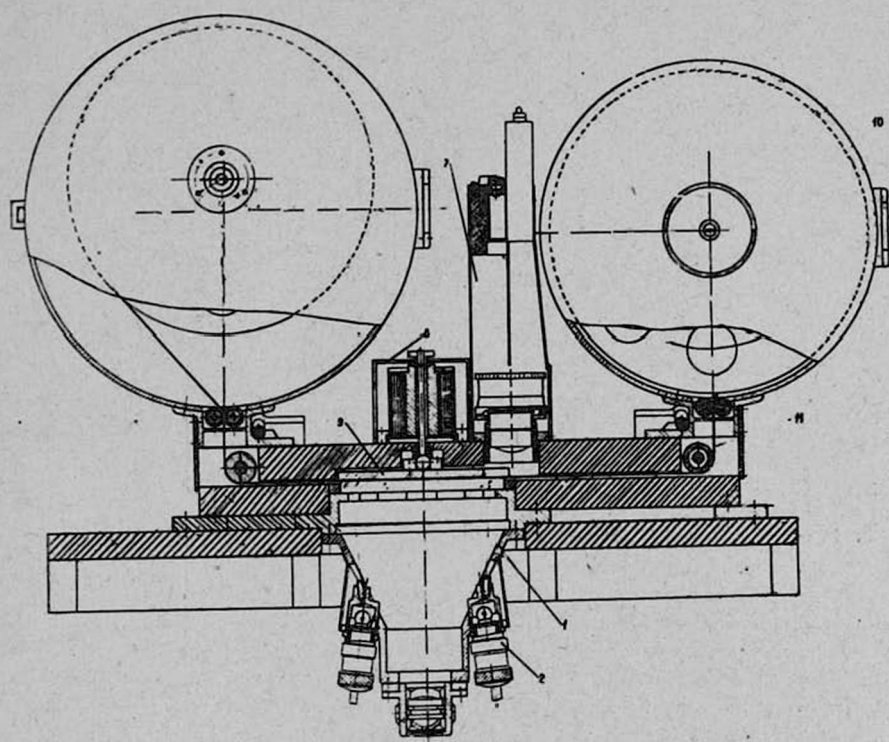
Схематический чертеж фотоаппарата. 1—корпус камеры КС-III, 2—лампочки подсветки крестов на предметном стекле, 3—объектив, 4—плата для фотокамер, 5—корпус фильмового канала, 6—подающая кассета, 6—блок цифровой системы, 8—электромагнит прижимного столика, 9—прижимной столик, 10—приемная кассета, 11—фотопленка.
